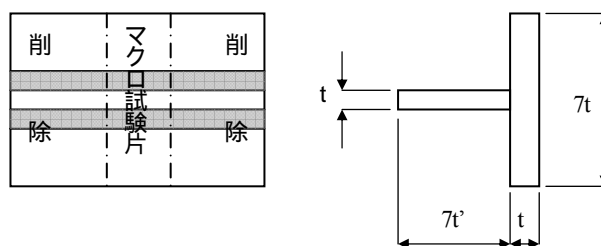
すみ肉溶接試験の試験体形状と試験片採取位置
